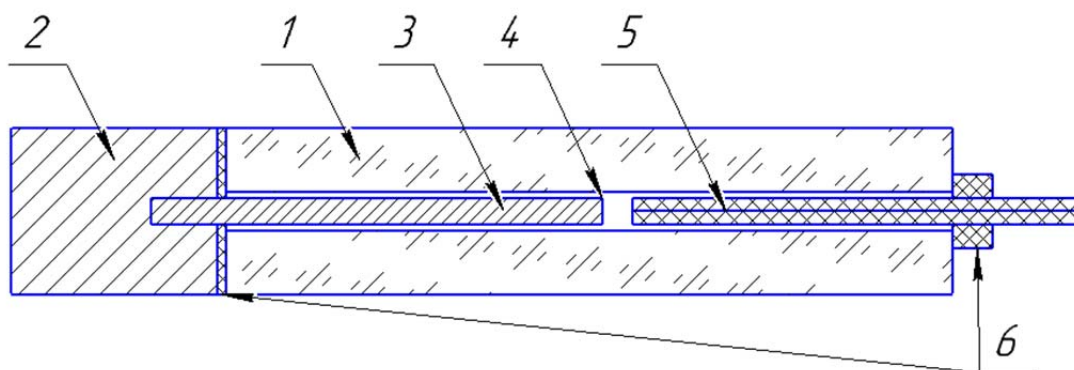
1 - стеклянный корпус (кварцевая трубка); 2 - металлический корпус (подставка); 3 - подвижный элемент (металлический стержень), 4 - отражатель (полированный торец стержня); 5 - керамический капилляр с двумя оптическими волокнами внутри - приемным и передающим, 6 оптический клей
